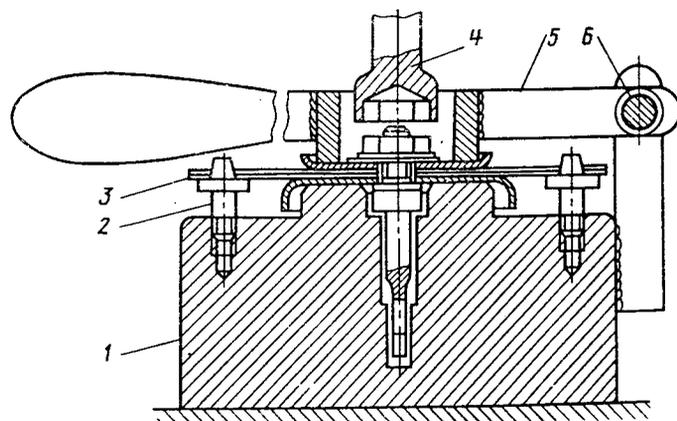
Vorrichtung zum Zusammenbau der Membran für Kraftstoffpumpe:
